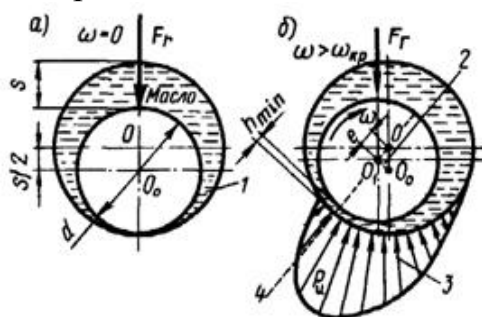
Гидродинамическая смазка подшипника скольжения
